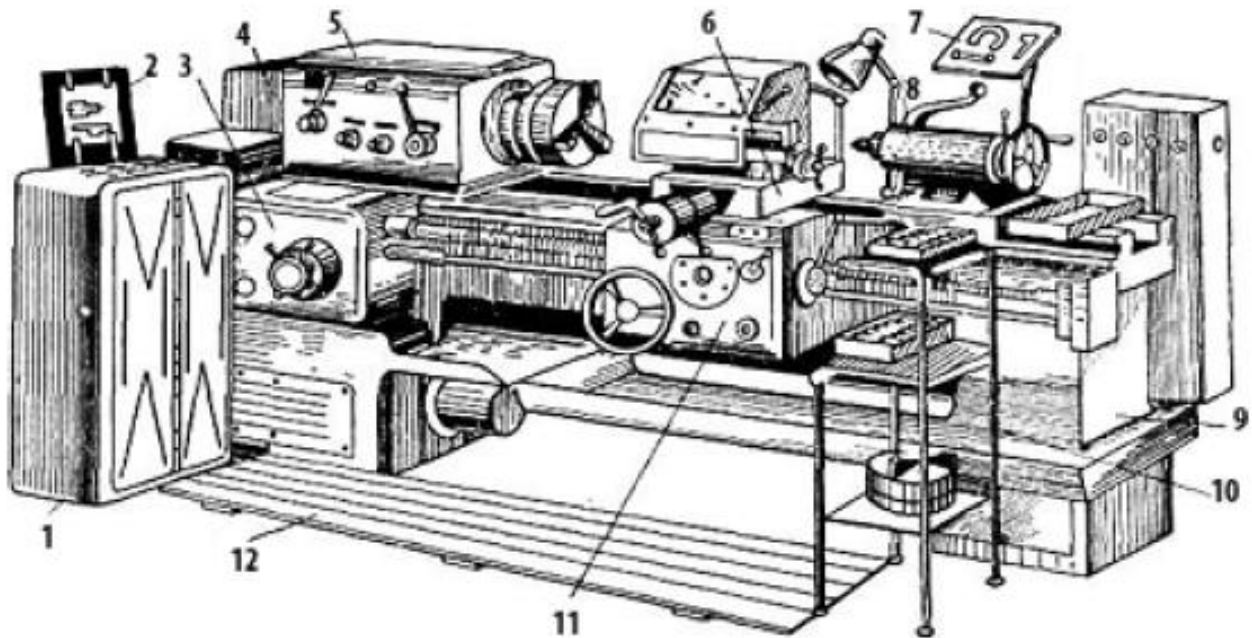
Токарно-гвинторізний верстат: 1 – тумба; 2- утримувач ескізу; 3 – коробка подач; 4 – гітара змінних зубчастих коліс; 5 – передня бабка; 6 – супорт; 7 – підставка для інструментів; 8 – задня бабка; 9 – станина; 10- тумба для інструментів; 11 – фартух; 12 – струмонепроводима підлога
